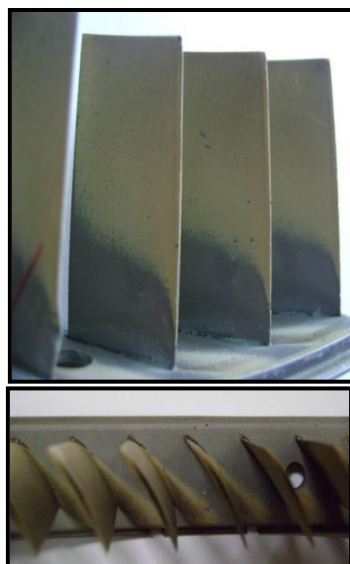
Общий вид лопаток НА: а – со стороны корыта, б – со стороны внутренней части бандажа
